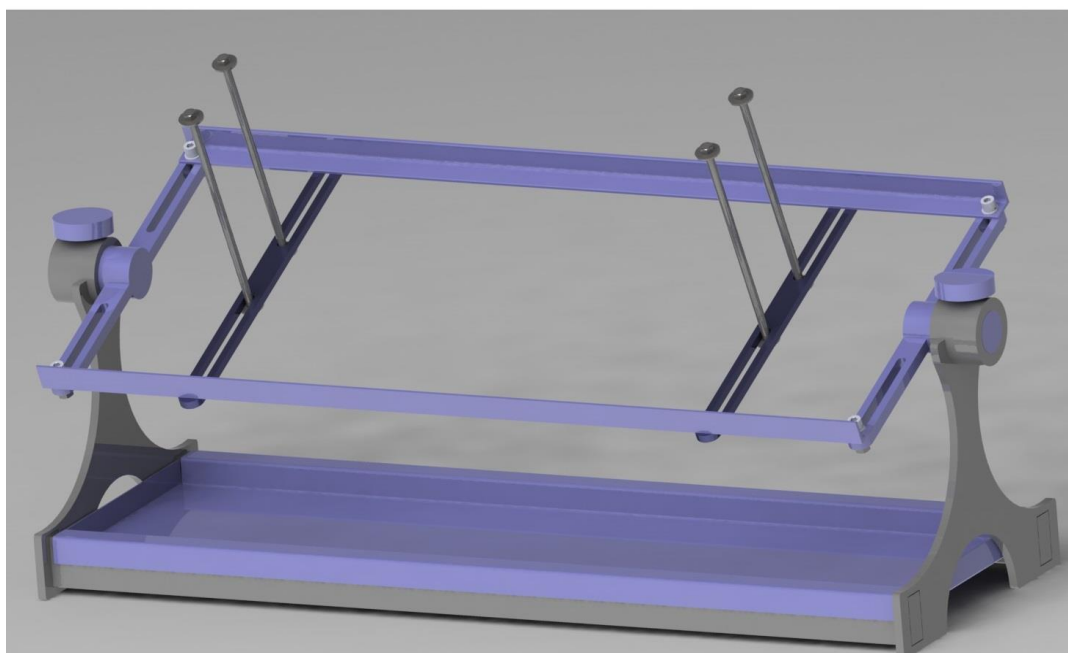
Стенд-кантователь головки блока цилиндров КГБЦ-1001
